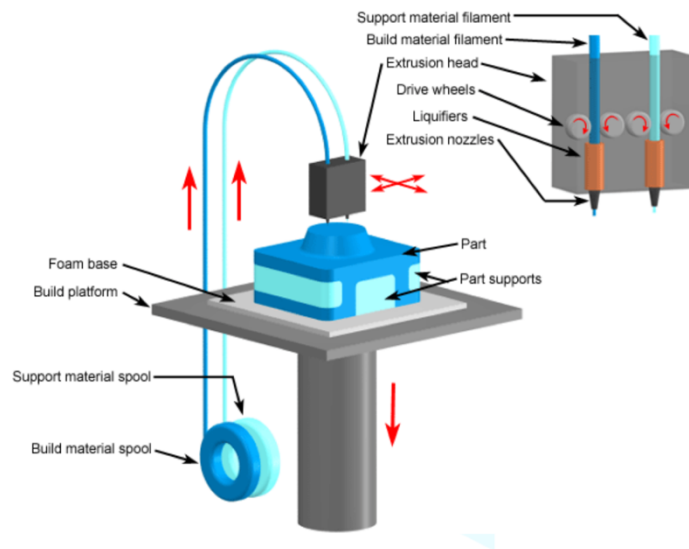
esquema de la técnica de Moldeo por Deposición de Fundidos (FDM).
